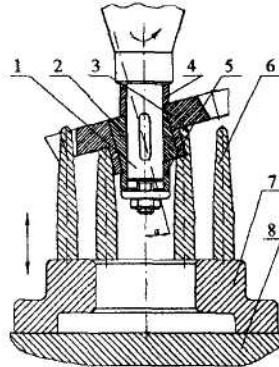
Схема спеціального пристосування для обробки зубів сателіта до вертикально-фрезерного верстата: 1 - оправка; 2 - коса втулка; 3 - сателіт; 4, 5 - косі шайби; 6 - інструменти; 7 - основа; 8 - стіл верстата
